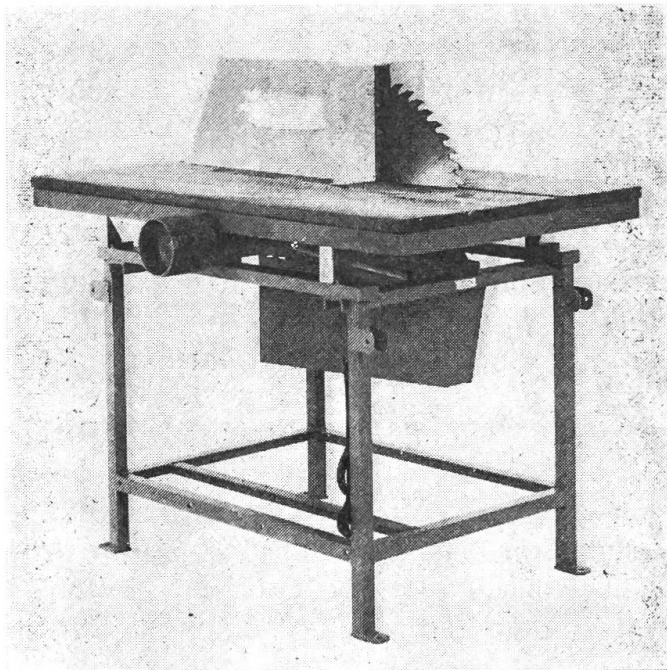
Korrekt abgedeckte Brennholzfräse: Schutzhaube mit Anschlag über dem Frästisch, abgedecktes Fräsblatt unten.
